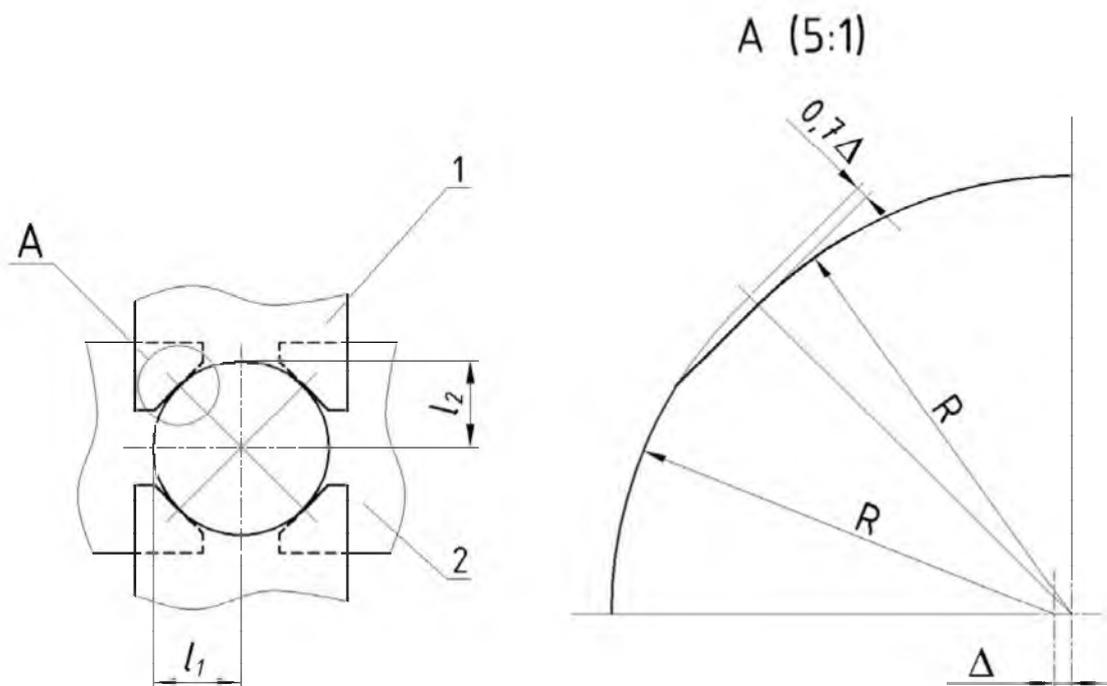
Схема формирования поперечного сечения цилиндрической детали при участии четырех фрез
